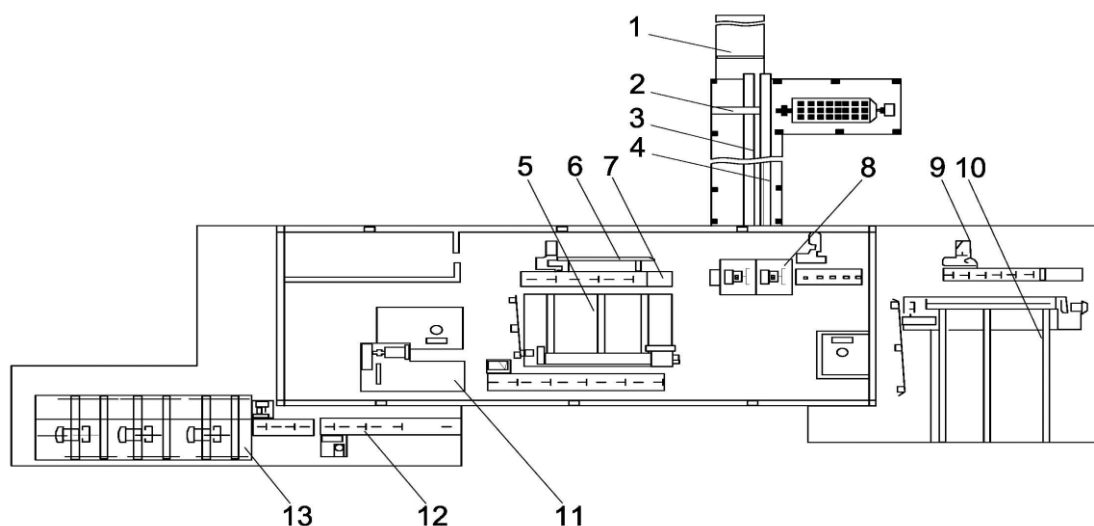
Линия для производства балансов [1]: 1 – контейнеры; 2 – лоток; 3, 4 – транспортеры стружки и коры; 5 – накопитель; 6 – сбрасыватель; 7 – конвейер позадистаночный; 8 – станок окорочный; 9 – конвейер цепной; 10 – питатель; 11 – установка раскряжевочная; 12 – транспортер сортировочный; 13 – устройство пакетоформирующее
